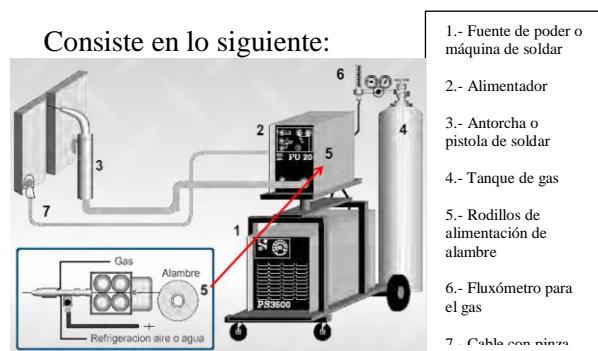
Diagrama del equipo de soldadura GMAW
